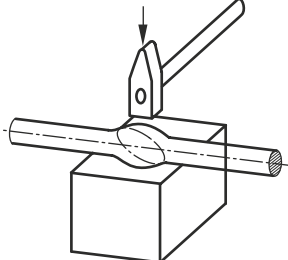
Wirkpaarungen beim Schweißen
